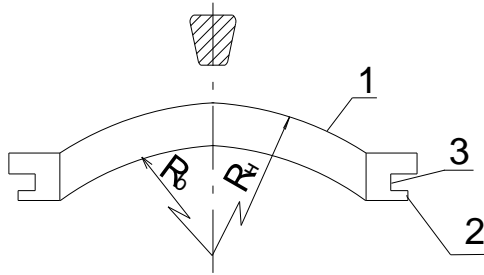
Конструкція колосника з трапецеїдальною формою робочої частини:
